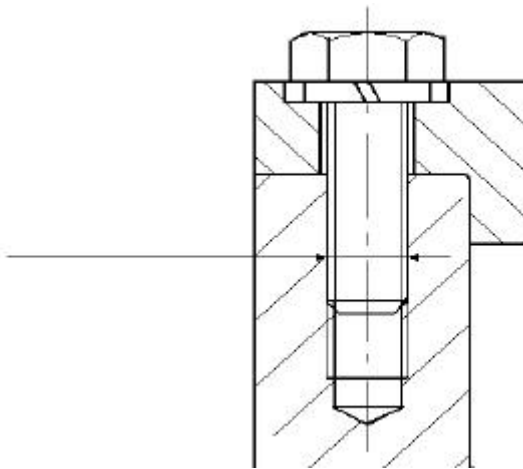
Обозначение внутренней резьбы на чертеже (вид сверху)
